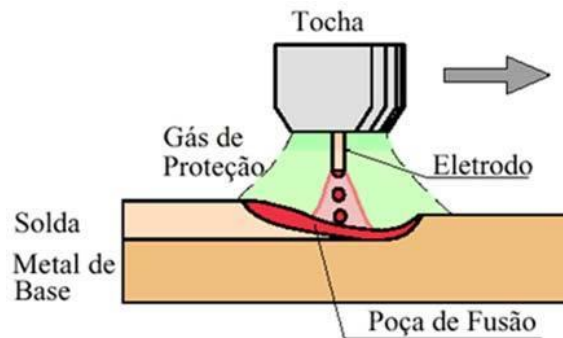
Representação de soldadura MIG-MAG.
